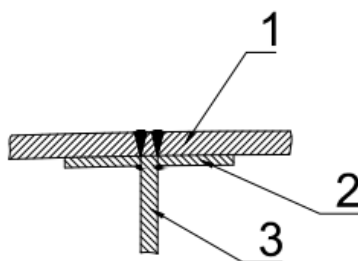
Приварювання зовнішньої обшивки до набору:
